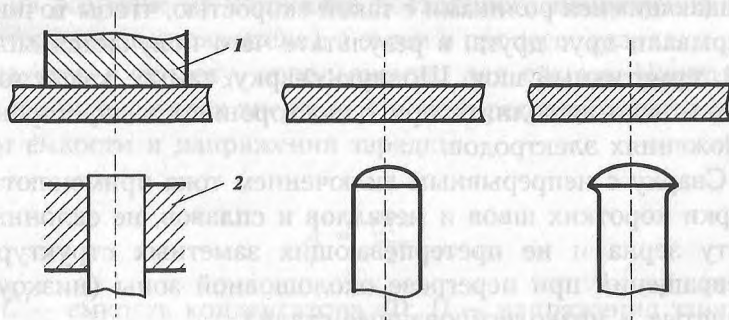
Схема Т-образной сварки: 1 — верхний электрод; 2 — нижний электрод
